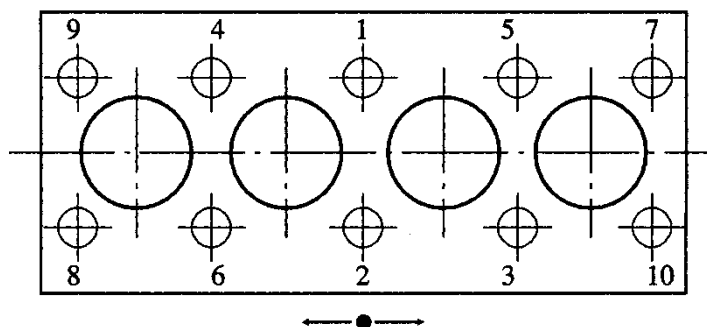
Последовательность затяжки болтов головки цилиндров.
